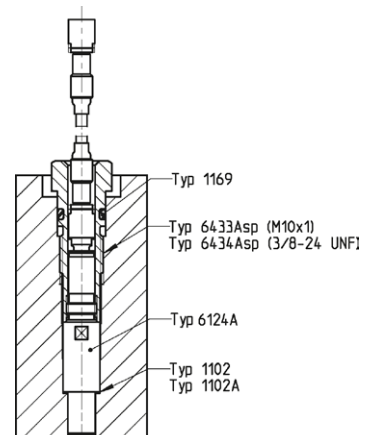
Einbau des Sensors Typ 6124A... mit Montagehülse
